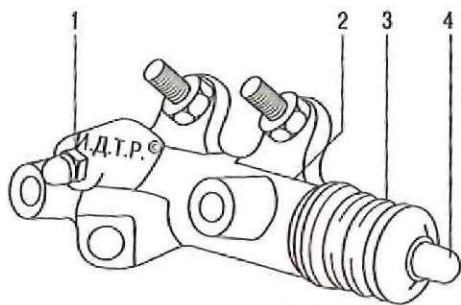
Рабочий цилиндр привода выключения сцепления: 1 – клапан для удаления воздуха; 2 – корпус; 3 – защитный колпачок; 4 – шток
